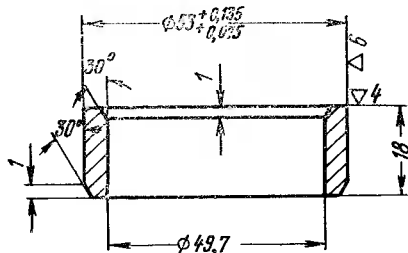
Ремонтная втулка отверстий вилок кардана под игольчатые подшипники
